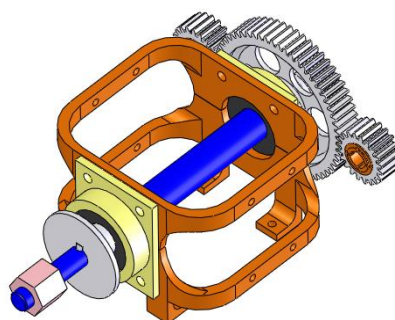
Desenho em CAD do primeiro protótipo de redução
